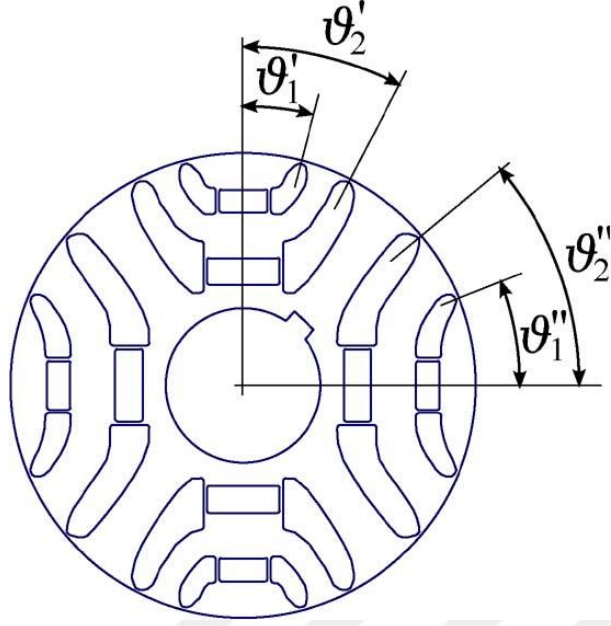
Farklı tasarımlardaki rotor geometrileri
